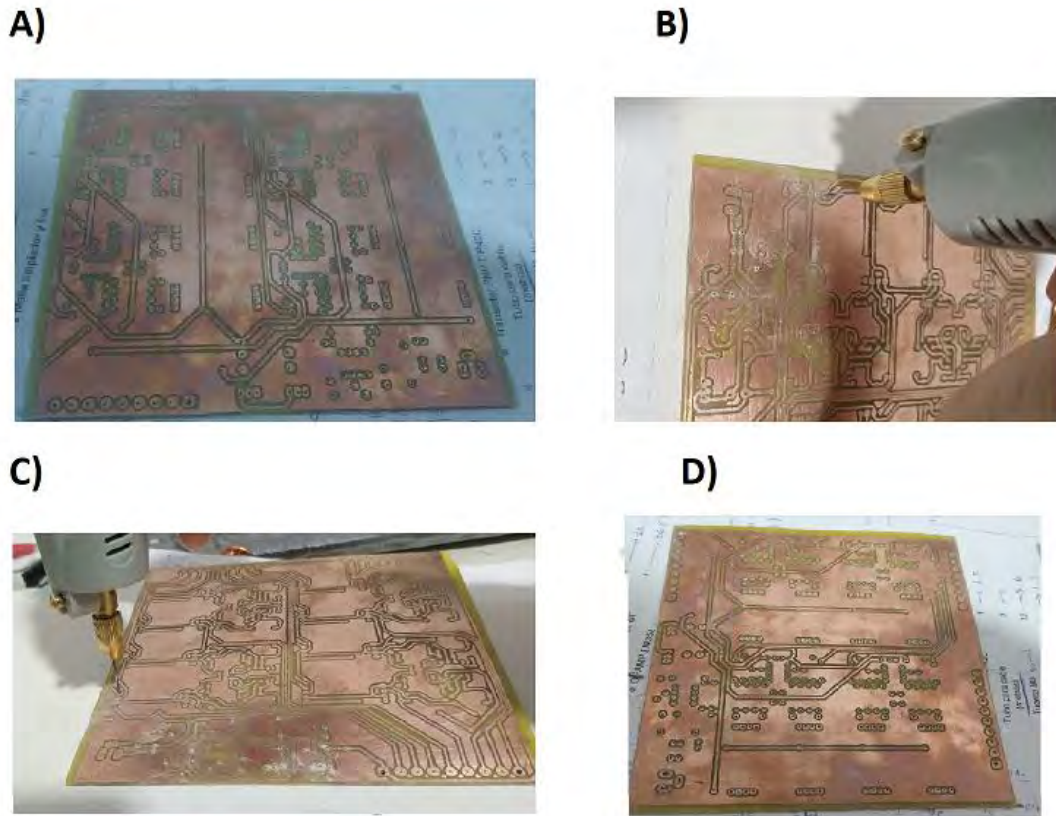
Preparación para proceso de soldadura. A) Placa sin residuos de papel después de pasar por ácido férrico. B) Realizando los primeros agujeros a la placa. C) Vista general durante el uso del mini taladro. D) Placa terminada lista para proceso de soldadura.
